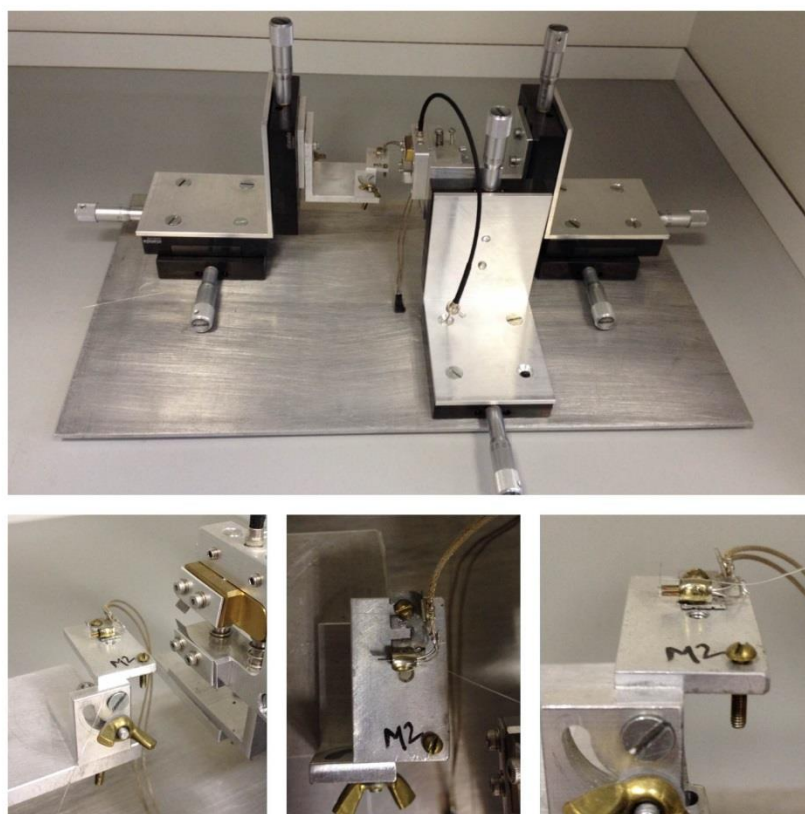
Приспособление для приклейки зонда к датчику контроля расстояния. Сверху: общий вид устройства. Нижний ряд слева направо: зонд с гильотиной для обрезки перемычки, крепеж держателя зонда (вид сверху), крепеж держателя зонда (вид спереди).
